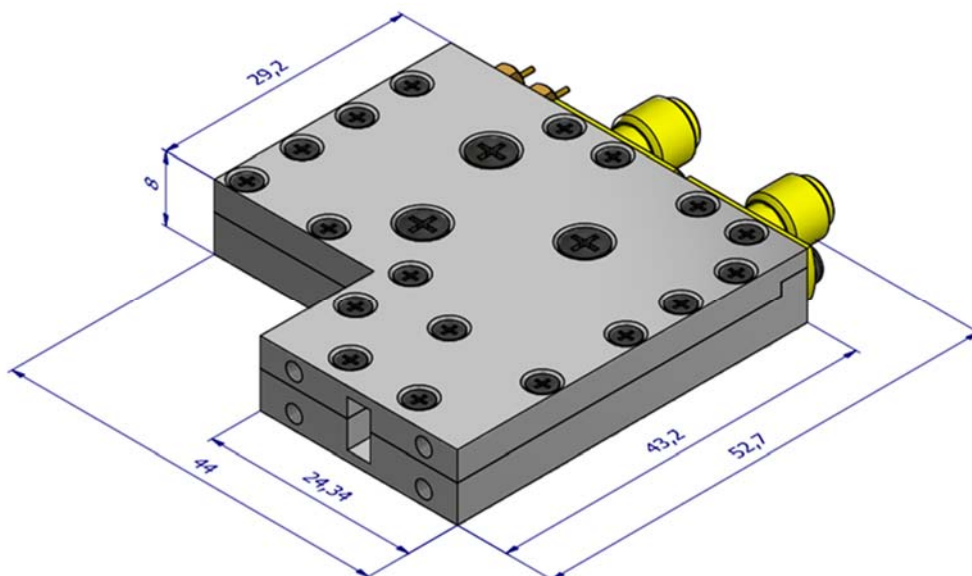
Dimensioni meccaniche del Q-CONV (in mm)
